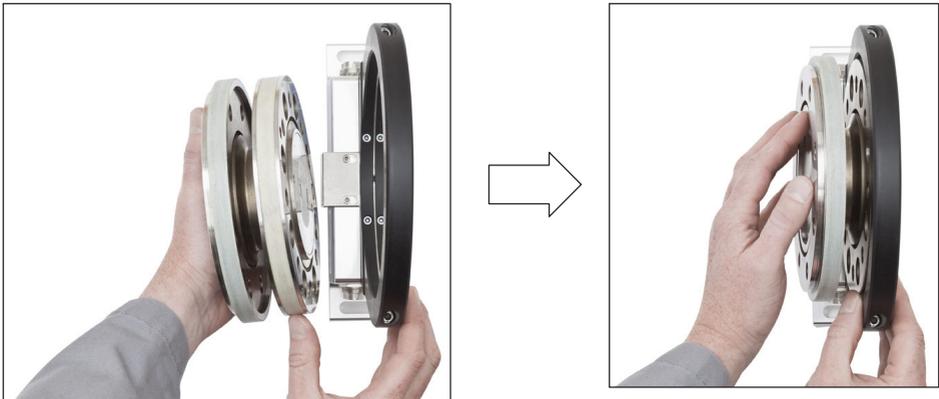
Ausrichten des Rotors mit dem Stator (ohne Referenzimpuls-Sensor)
